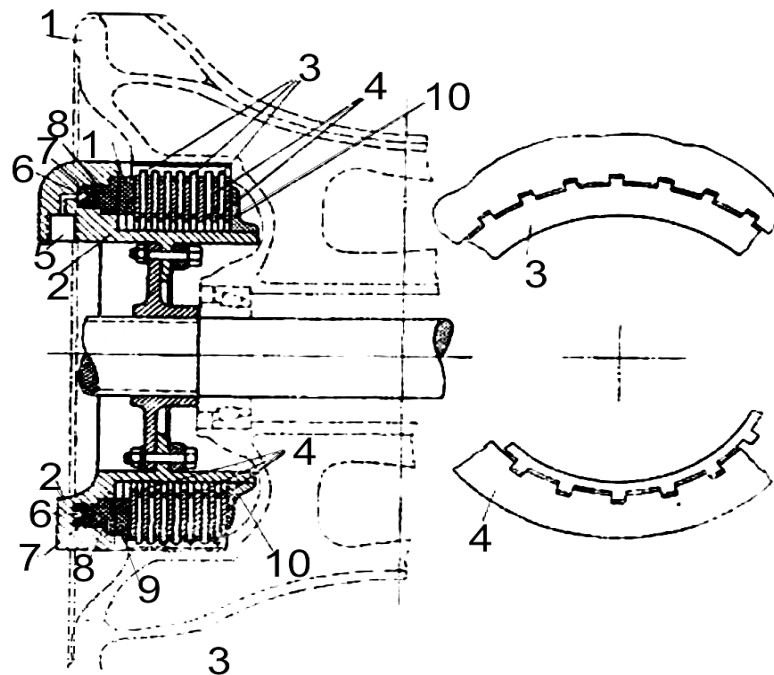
Дисківе гальмо: 1 – корпус колеса; 2 – корпус барабана; 3 – диски, що обертаються; 4 – нерухомі диски; 5 – канал для рідини; 6 – кільцева порожнина; 7 – гумове кільце; 8 – кільцевий поршень; 9 – кільцевий диск; 10 – кільцева регулювальна шайба
